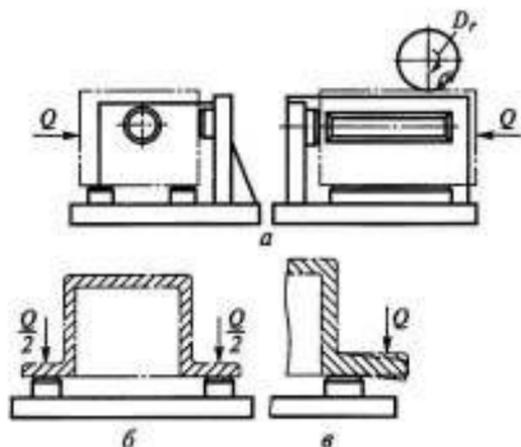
Схема закрепления детали: a и b — правильно; $в$ — неправильно; Q — усилие зажима; D_r — направление движения резания
